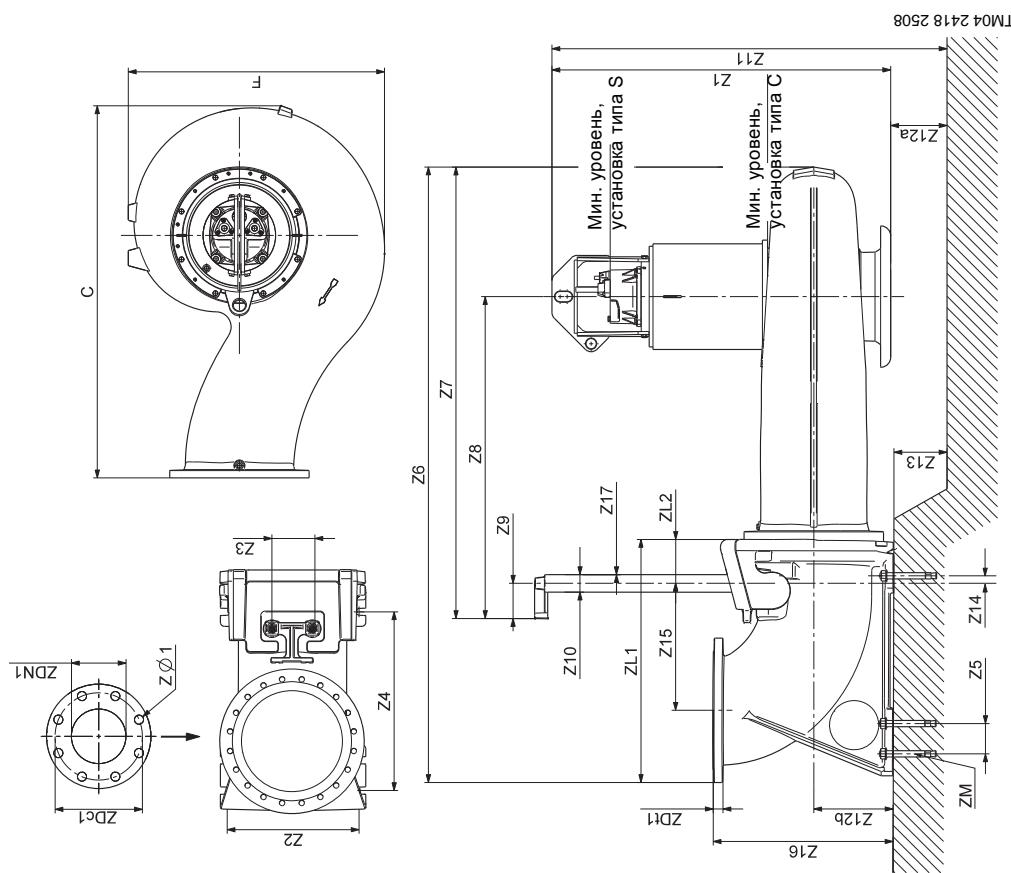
Габаритные размеры, установка на автоматической трубной муфте
